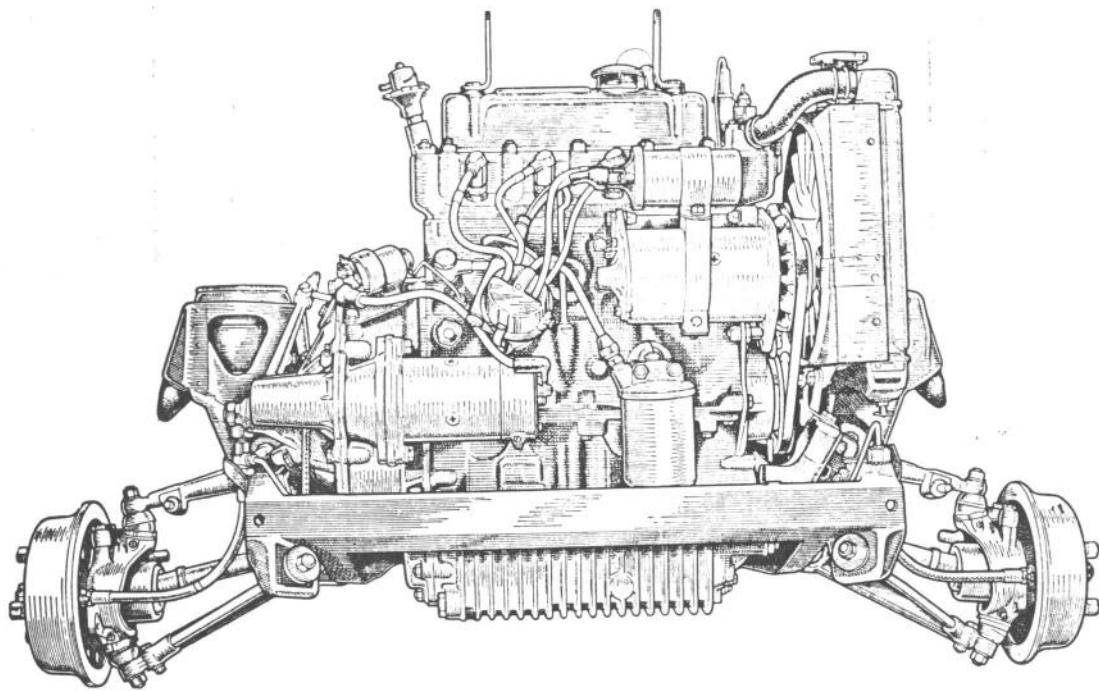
Vista delantera del motor y de la suspensión delantera.
